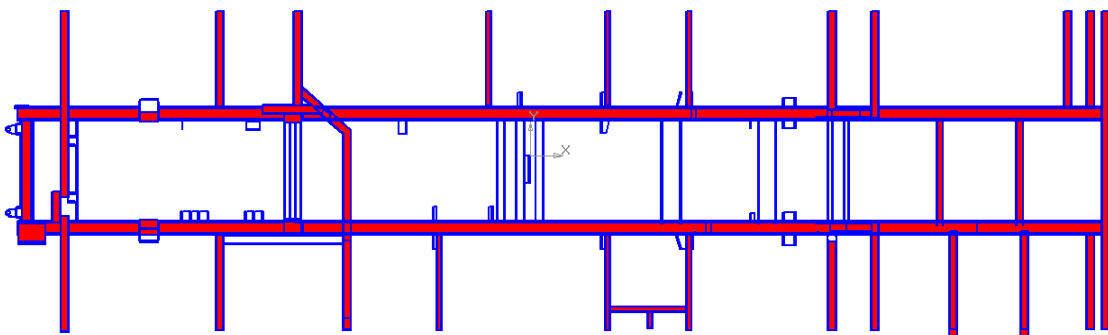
Схема нанесення антикорозійної захисної рідини у внутрішні поверхні труб основи автобуса (вид зверху)
